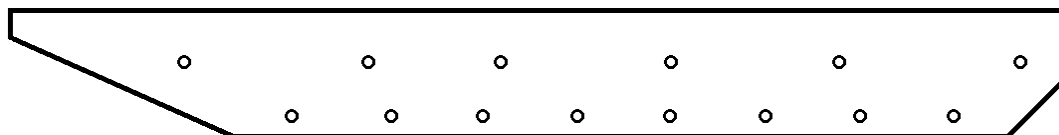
Герметичный полый корпус тягача (вид сбоку)
